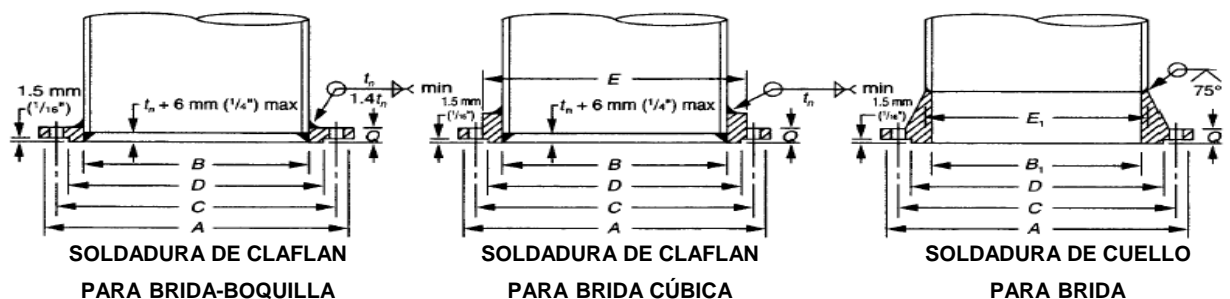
Tipo de soldadura para Bridas²⁰
